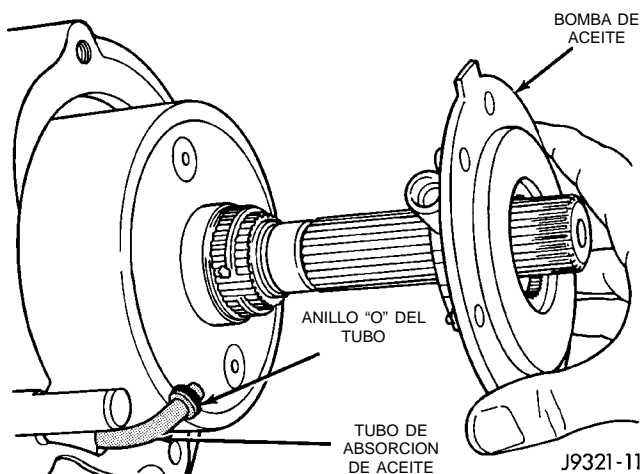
Desmontaje de cojinete trasero y bomba de aceite
